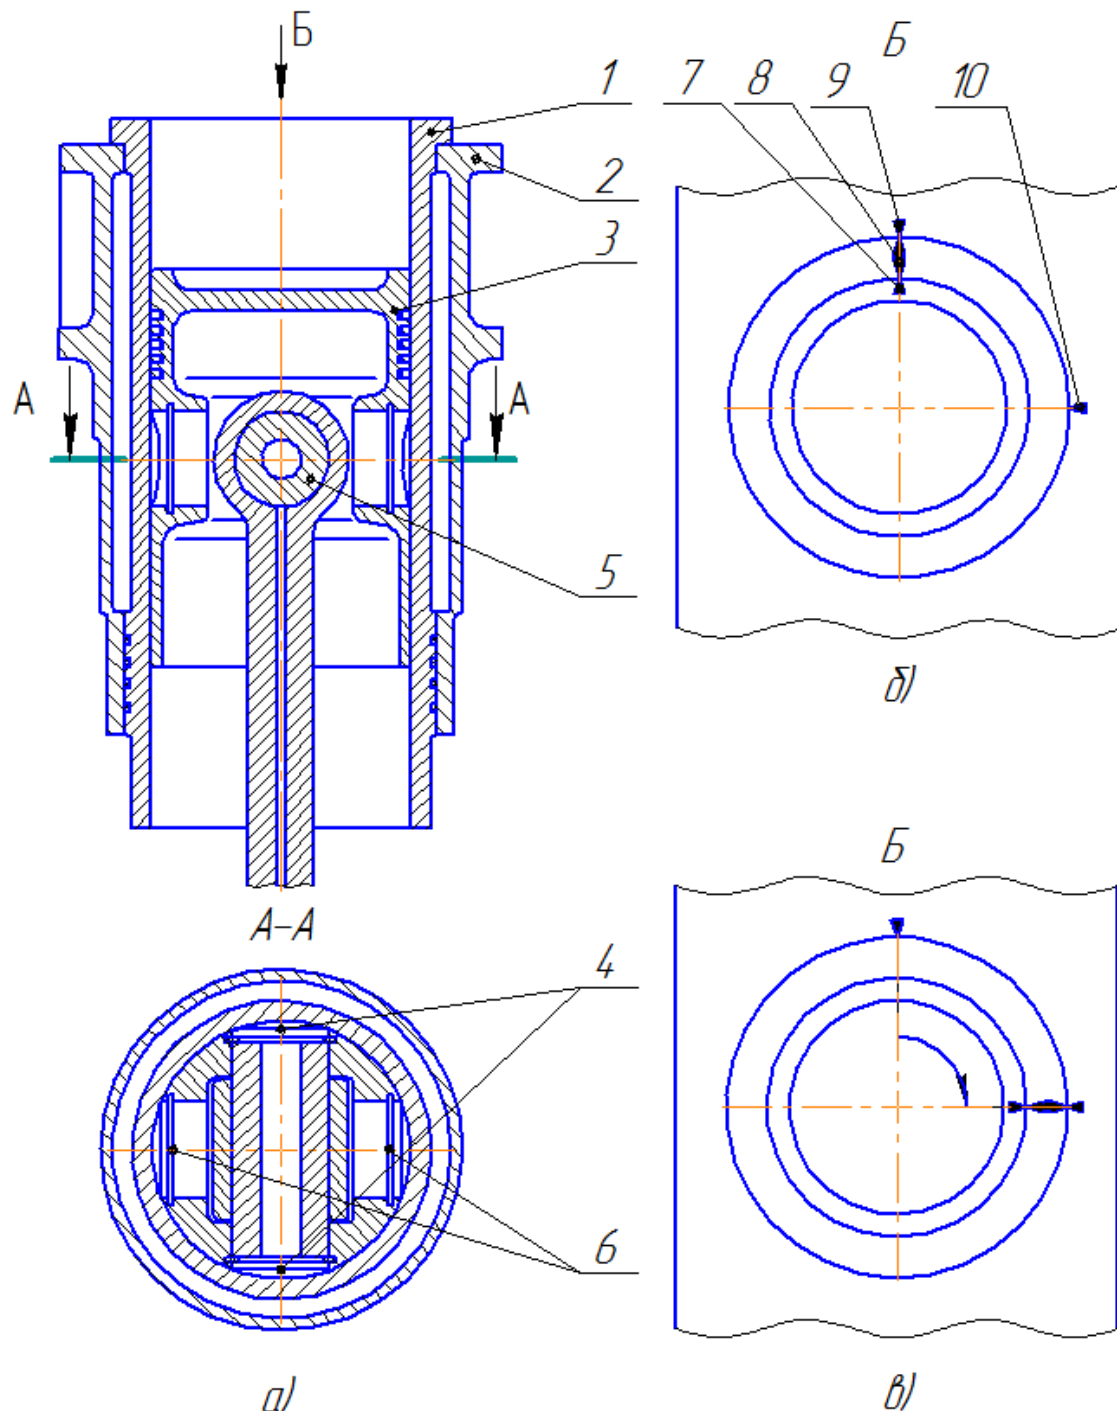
Циліндро-поршнева група тронкового двигуна:
